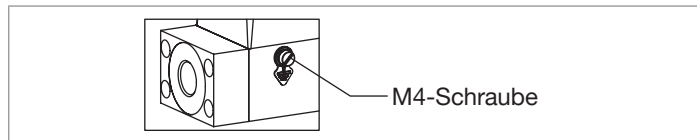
Position der M4-Schraube für den Anschluss des Funktionserdungskabels
